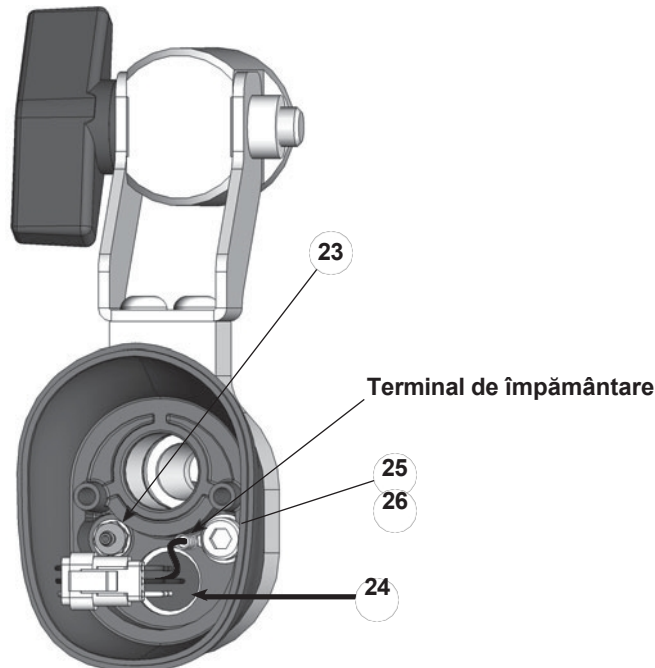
Pistol Demontare - Înlocuirea receptorului de cablu și a fittingului cu barbă
